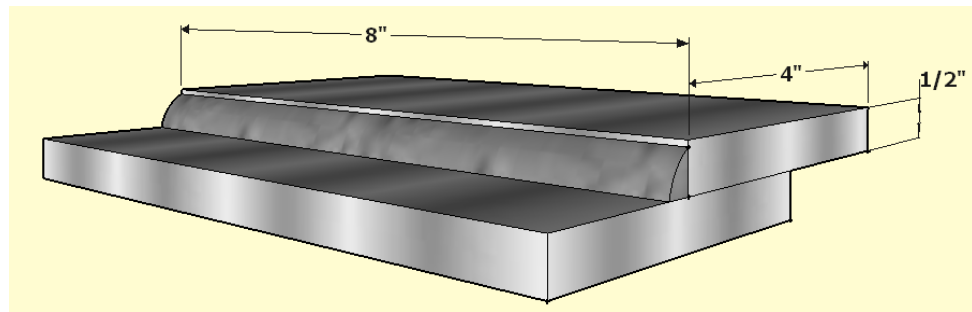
2 Placas traslapadas unidas mediante soldadura de filete.
